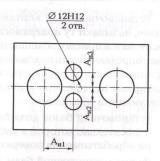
Эскиз обрабатываемой детали к заданию 1.29
